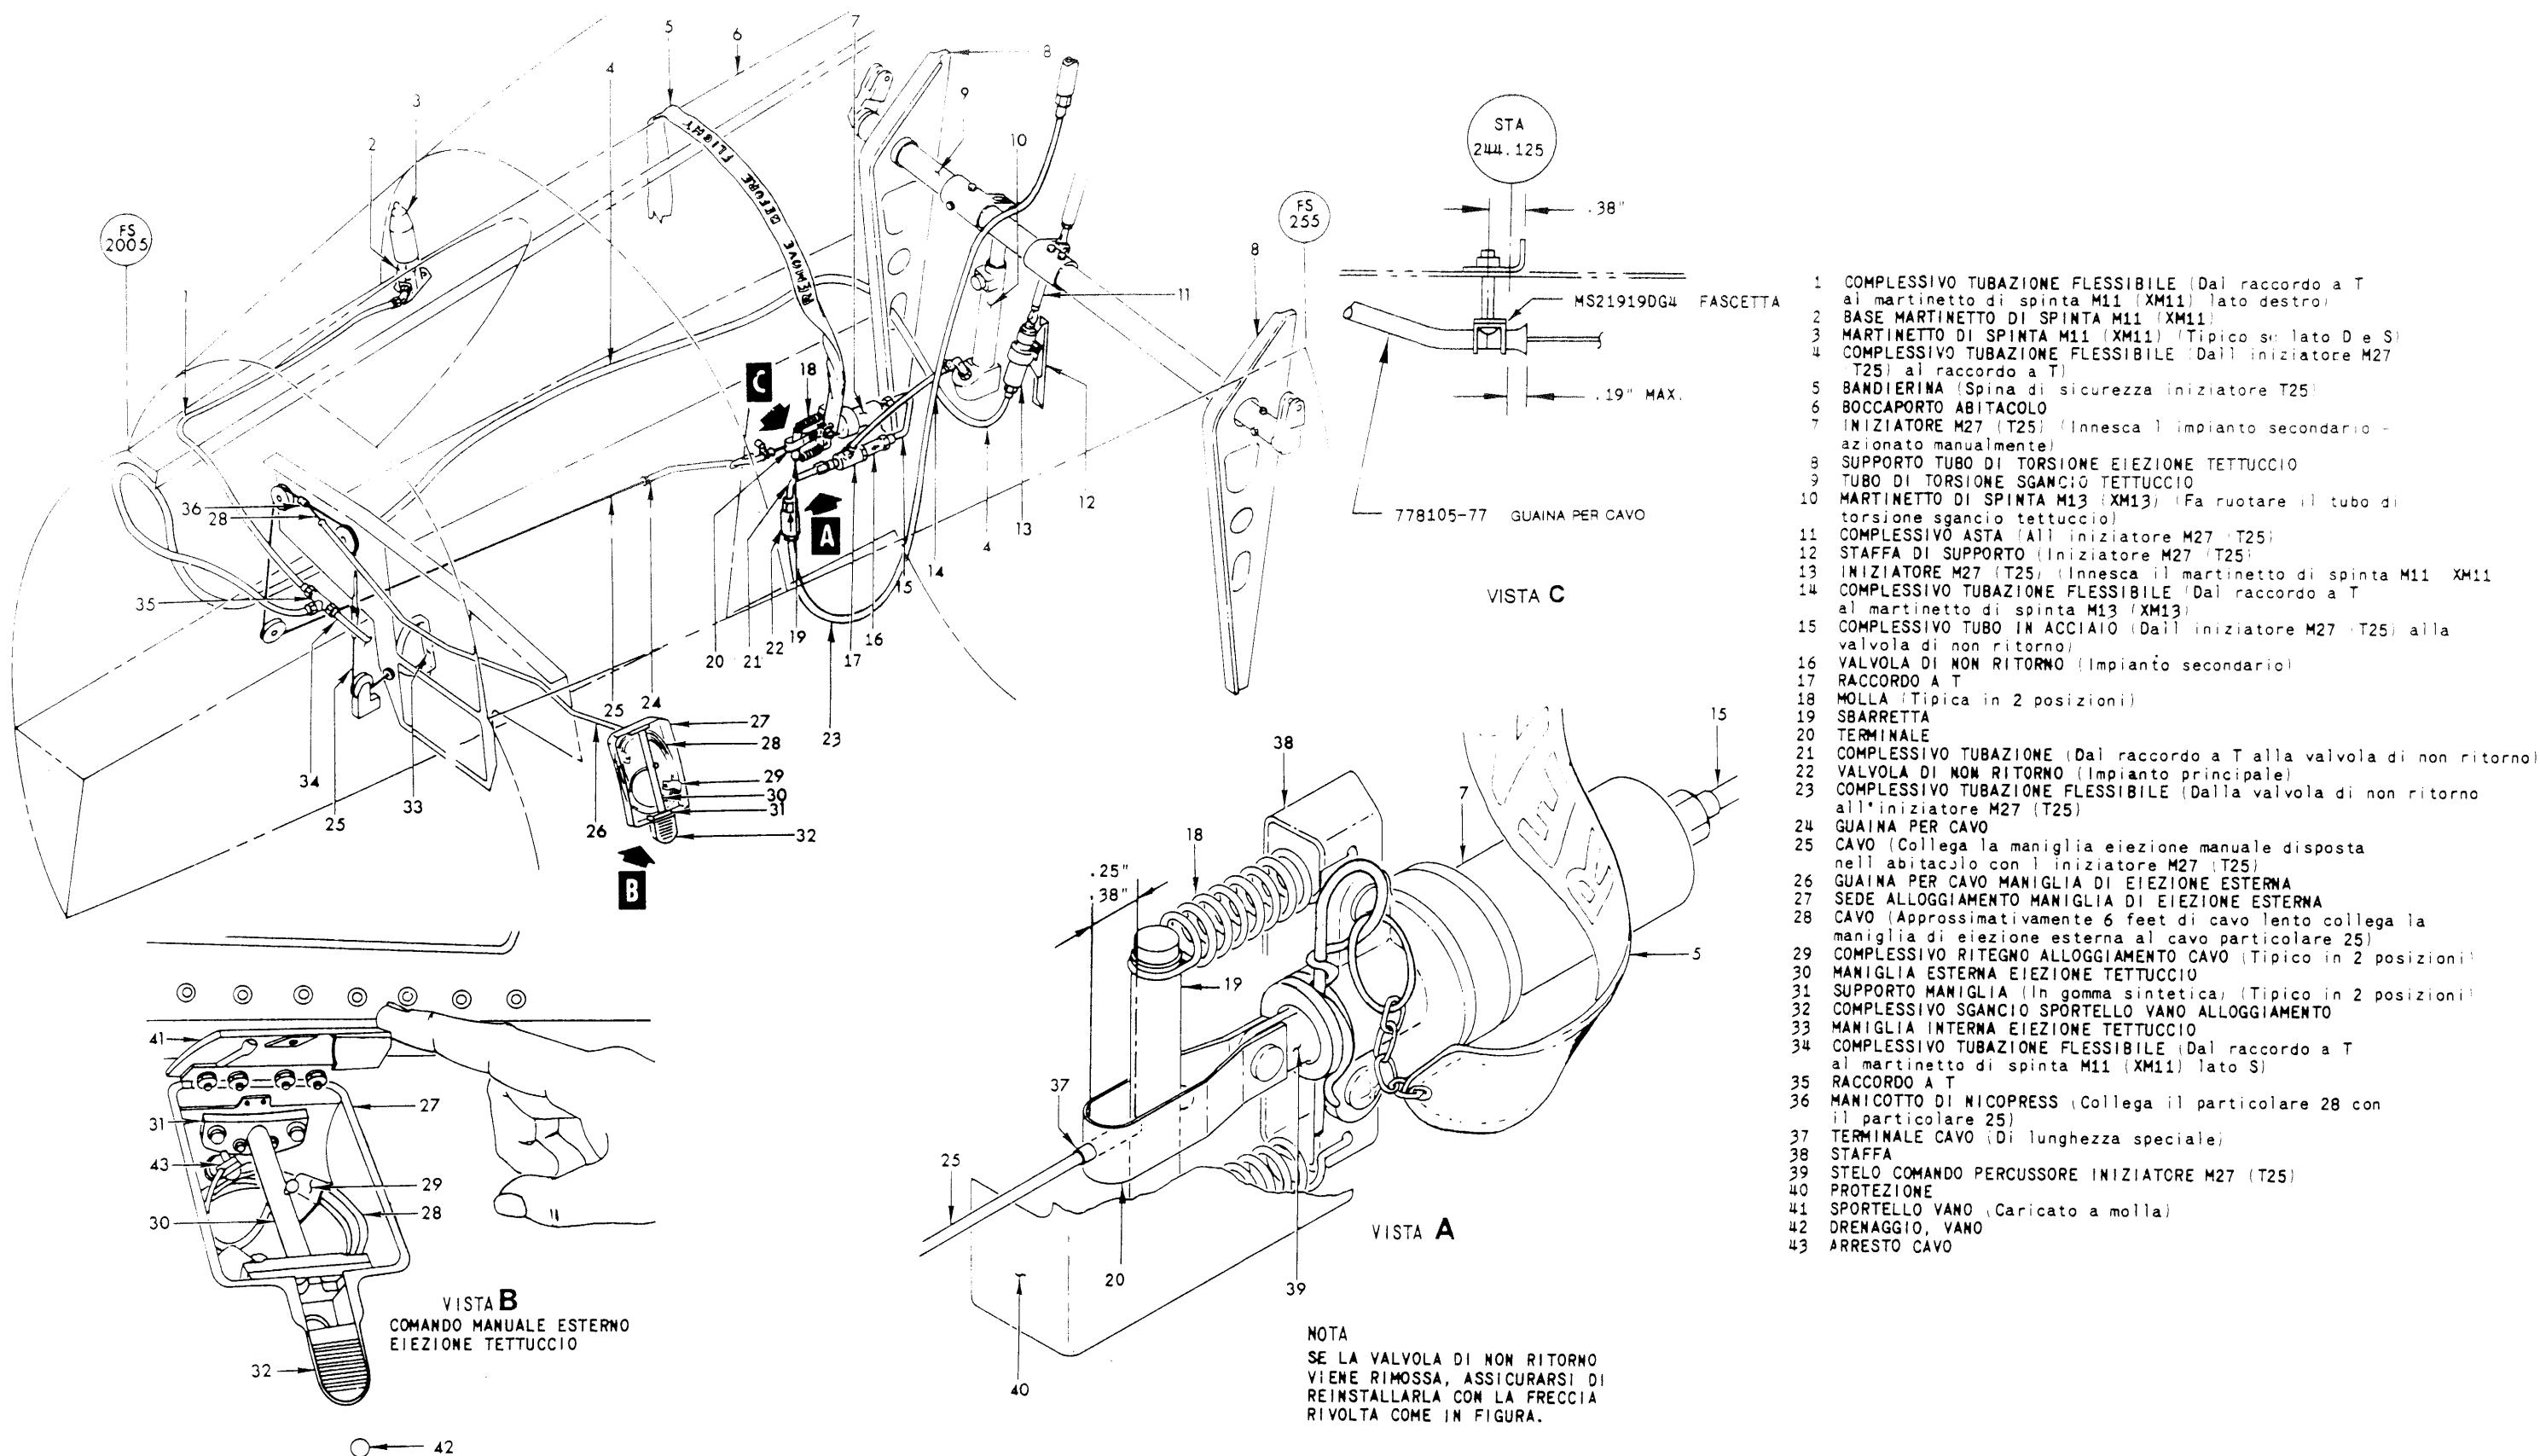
Funzionamento impianto eiezione tettuccio.
